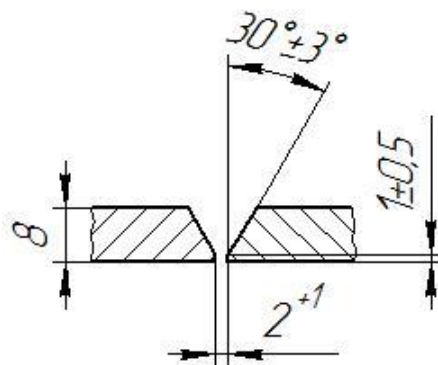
Требования к подготовке кромок и сборке стыка перед сваркой
